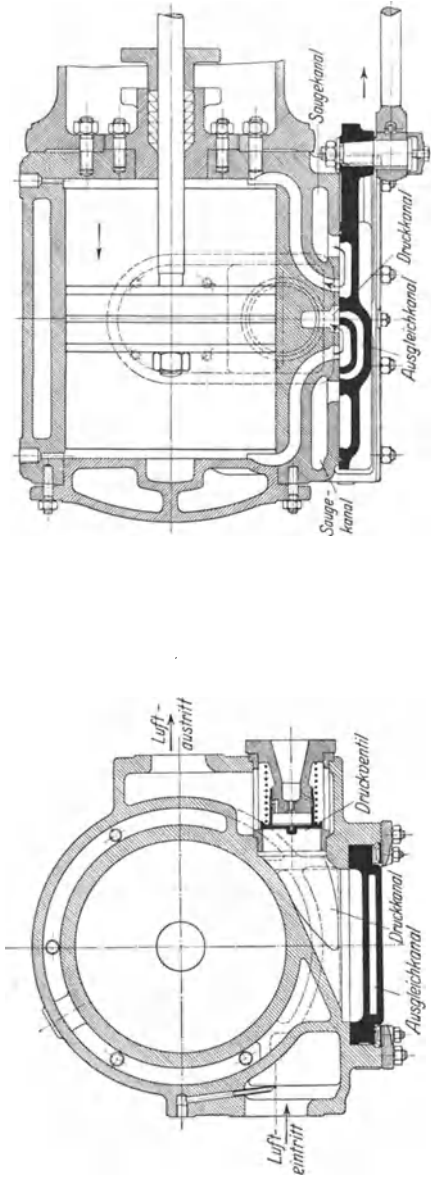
und 218. Trockenluftpumpe mit Druckausgleich von Köster der Frankfurter Maschinenbau A.-G.
